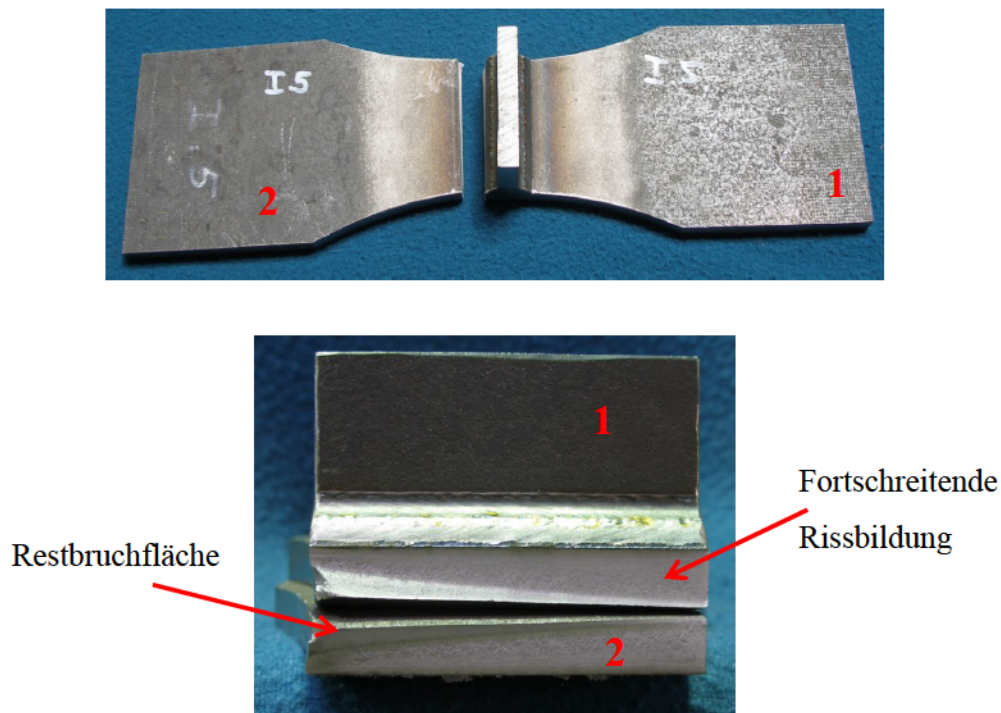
Bruchfläche des Schweißzustandes (Gruppe I)
